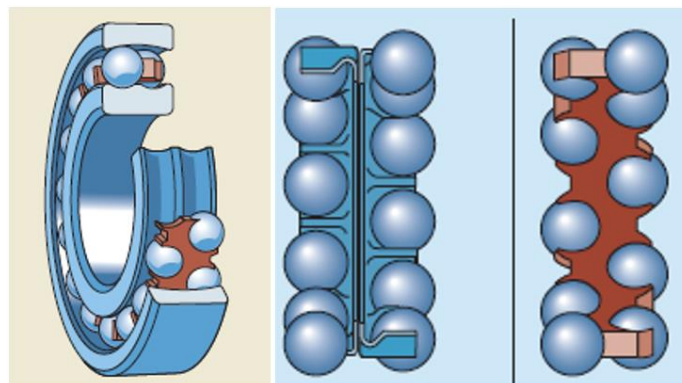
Rodamientos de bolas a rotulas. Tomada de Catálogo de rodamientos SKF
